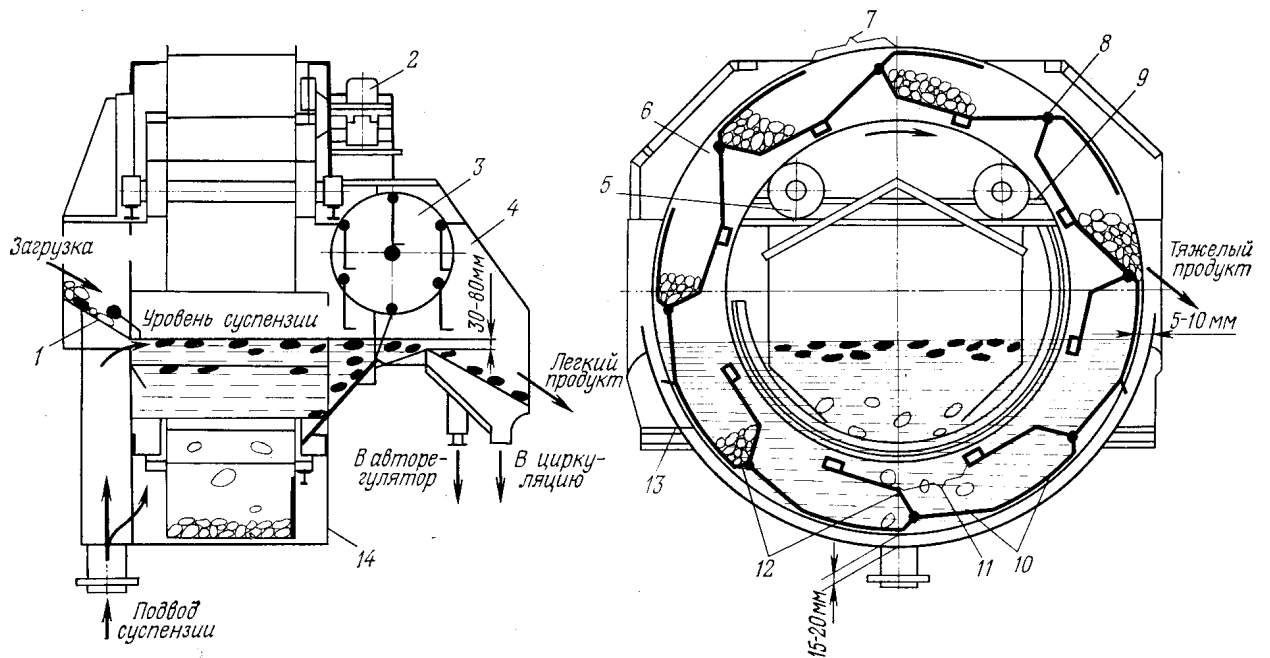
Сепаратор СКВ: 1 – загрузочный желоб; 2 – привод элеваторного колеса; 3 – гребковое устройство; 4 – концентратный желоб; 5 – опорные катки; 6 – элеваторное колесо; 7 – разгрузочное окно; 8 – шарнир поворотной решетки; 9 – опора опорных роликов; 10 – стенки ячейки элеватора; 11 – загрузочное окно; 12 – порода
